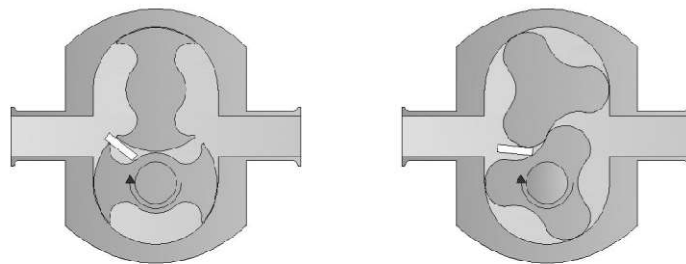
Rotorschrauben festziehen (unterer Rotor)
